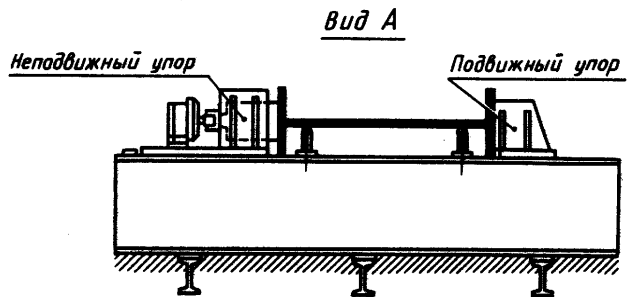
Установка для сборки балок H-образного сечения с самоходным сборочным порталом
